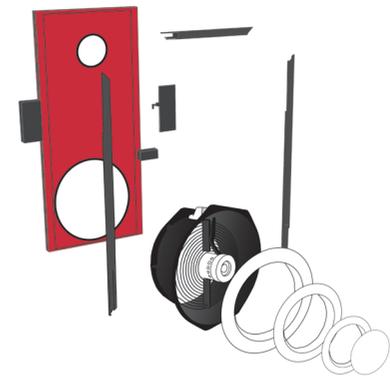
Anillos para controlar el área de apertura del ventilador, Equipo Q4E Blower Door Retrotec.
